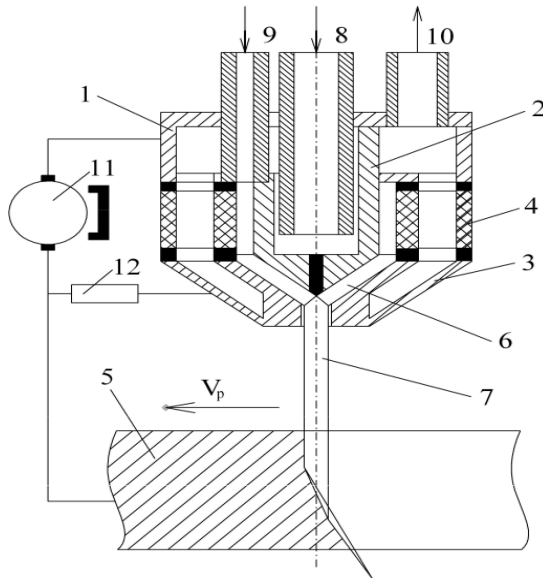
Режущий плазмотрон: 1 – корпус; 2 – электрод (катод); 3 – формирующий наконечник; 4 – изолятор; 5 – разрезаемый металл; 6 – дуговая камера; 7 – столб дуги; 8 – подача охлаждающей воды; 9 – подача плазмообразующего газа; 10 – слив воды; 11 – источник тока; 12 – устройство зажигания дуги;  $V_p$  – направление резки
